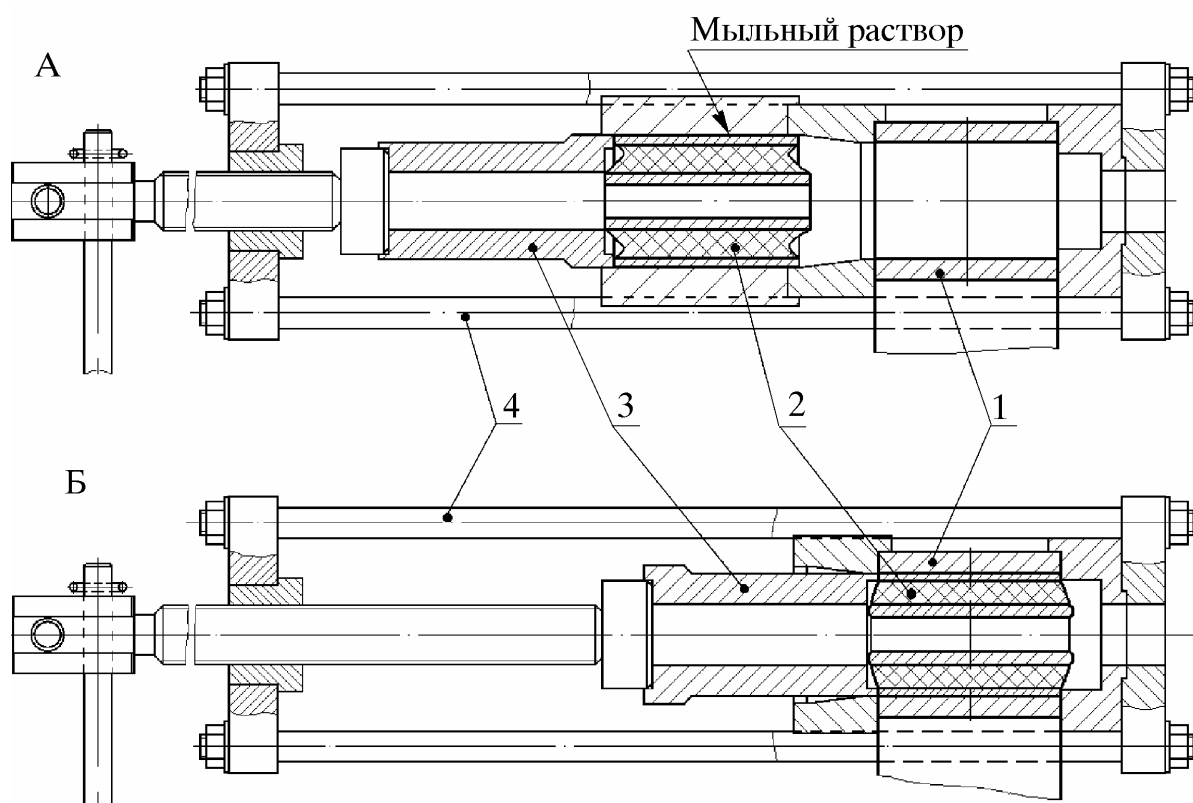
Запрессовка резинометаллического шарнира в ушко рессоры:
